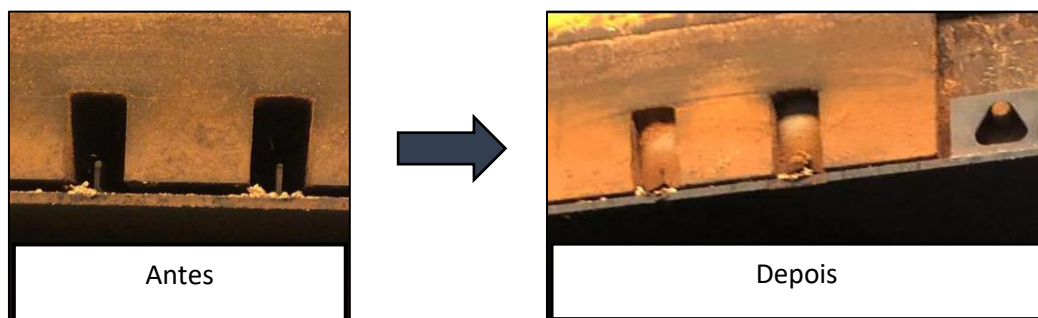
Situações Antes e Depois do preenchimento do espaço vazio entre a prensa e as chapas
